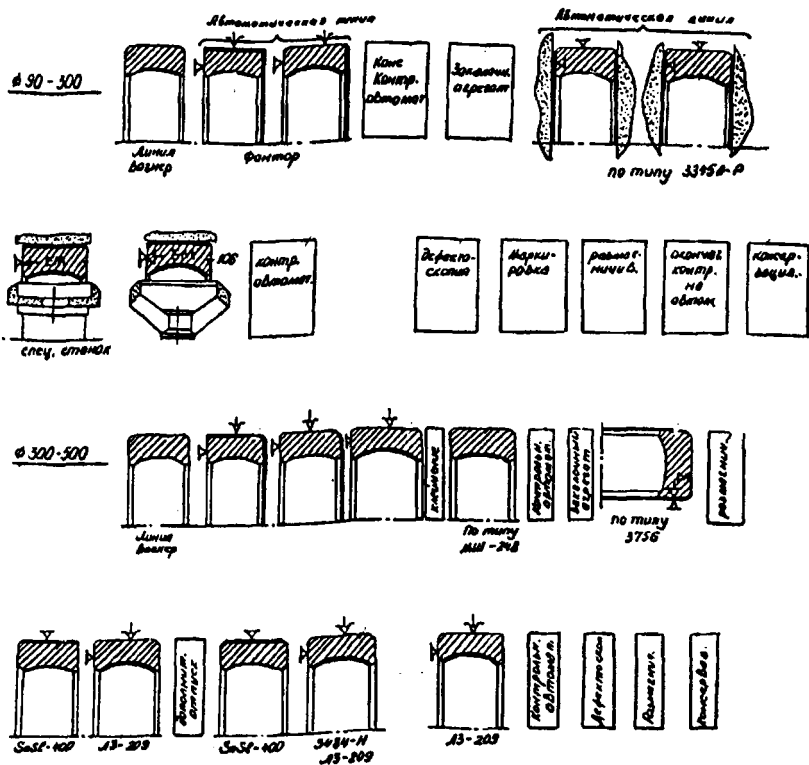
Перспективный процесс механической обработки наружных колец роликовых сферических подшипников
